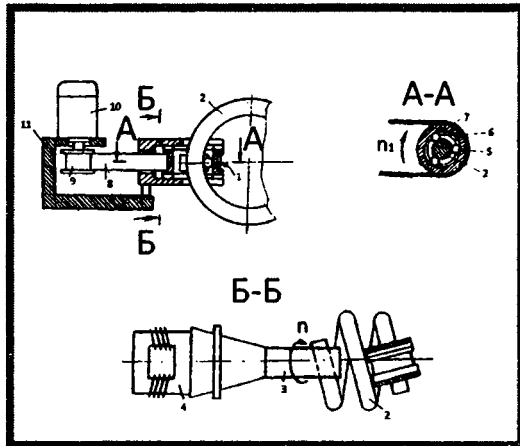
Схема устройства для упрочняюще-чистовой обработки деталей типа винтовых пружин
